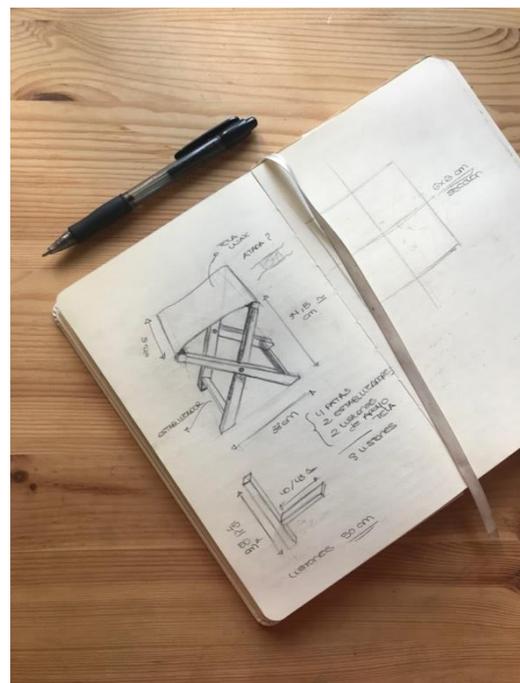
SKETCH EN LA LIBRETA DE SILLA PLEGABLE. FUENTE: PROPIA
